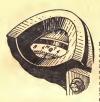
Установка коленчатого вала автомобили ГАЗ-51 (в положении поршия первого цилиндра в в. м. т.).
